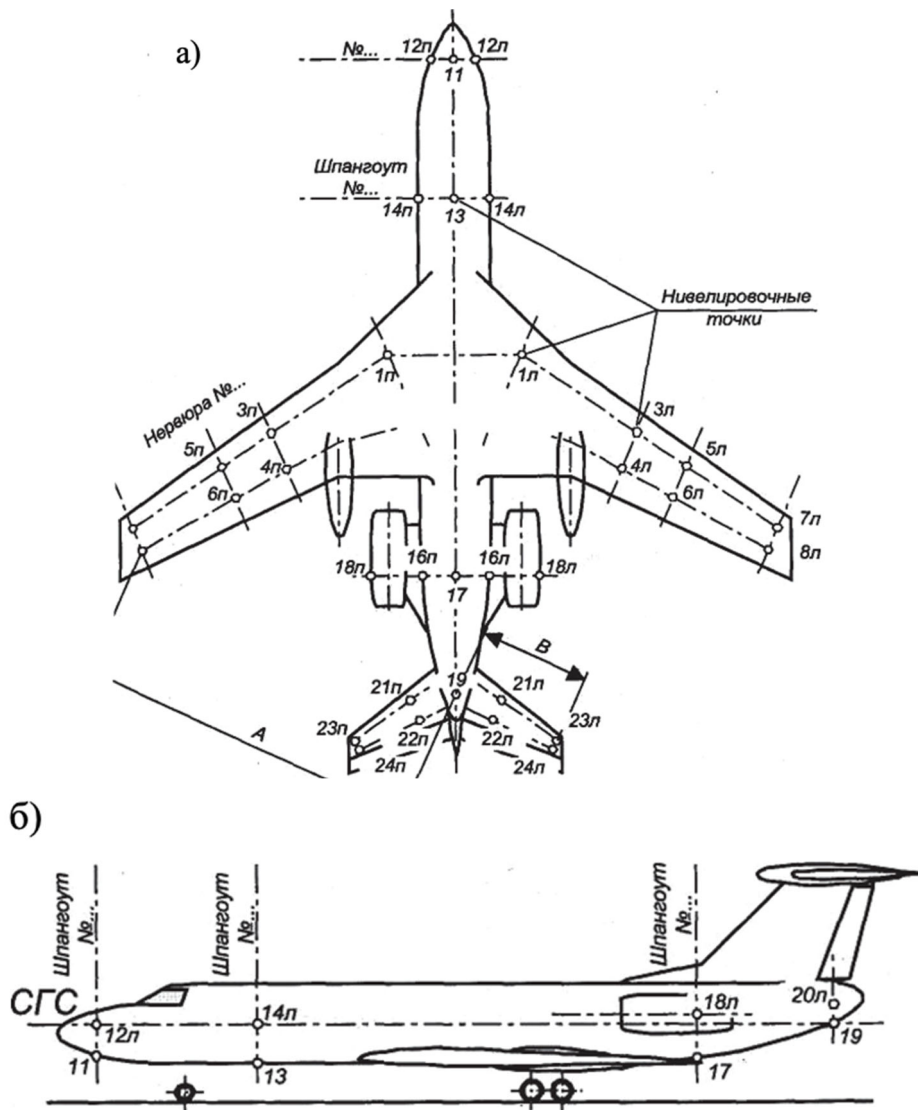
Фрагмент нивелировочного чертежа самолета: а) вид сверху;
